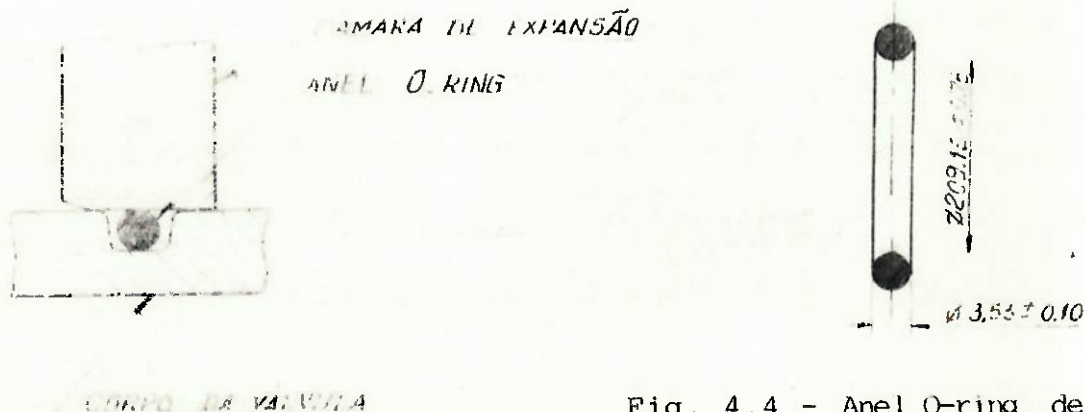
Esquema de posicionamento do Anel O-ring
